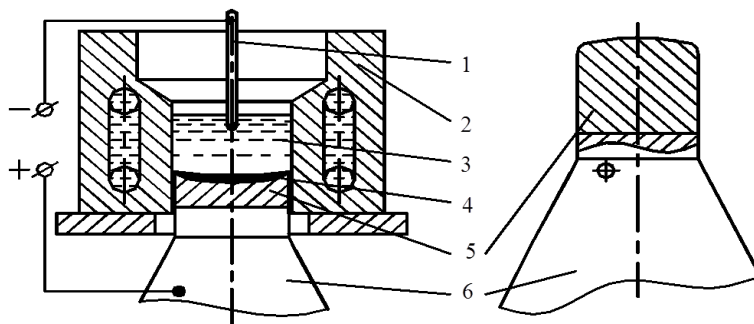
Схема наплавки носка оправки: 1 — электрод; 2 — кристаллизатор; 3 — шлаковая ванна; 4 — металлическая ванна; 5 — наплавленный металл; 6 — основной металл
